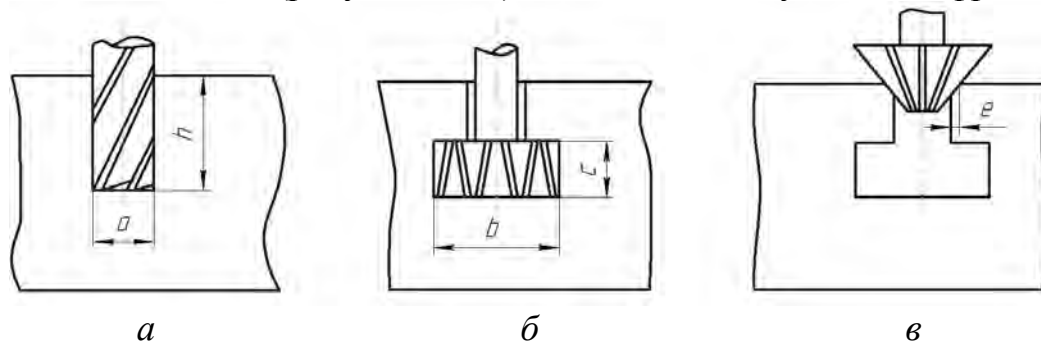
Последовательность фрезерования Т-образного паза
